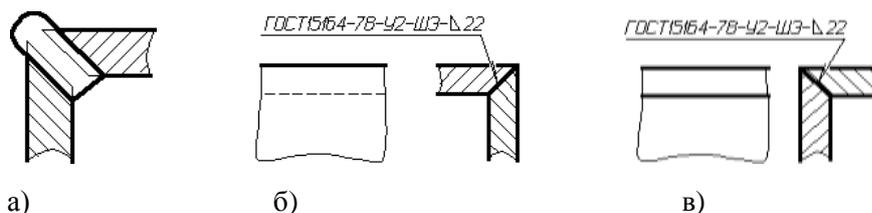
Шов углового соединения со скосом кромок, выполненный электрошлаковой сваркой: а) форма поперечного сечения шва; б) с лицевой стороны; в) с оборотной стороны
